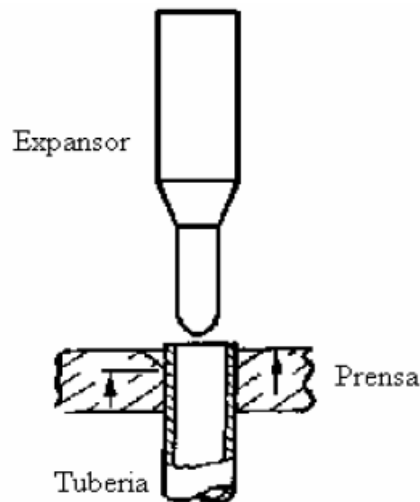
Herramienta para abocardar tubo de cobre y de sección circular.
